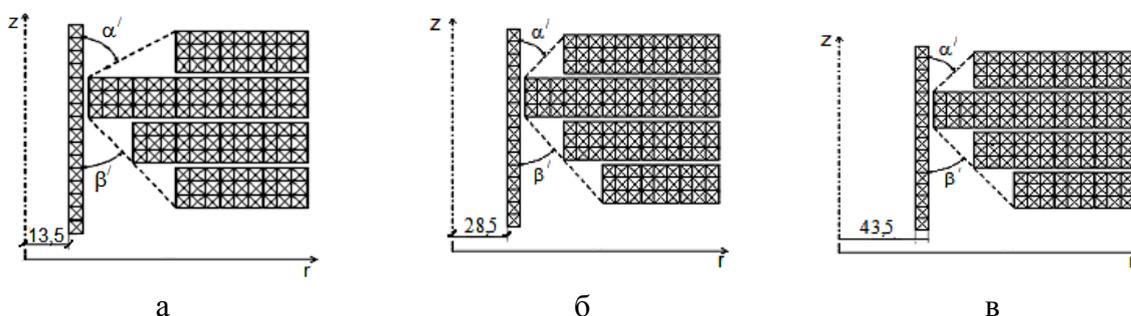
Геометрия индуктора-концентратора при обжиге алюминиевой заготовки с внутренним радиусом:
